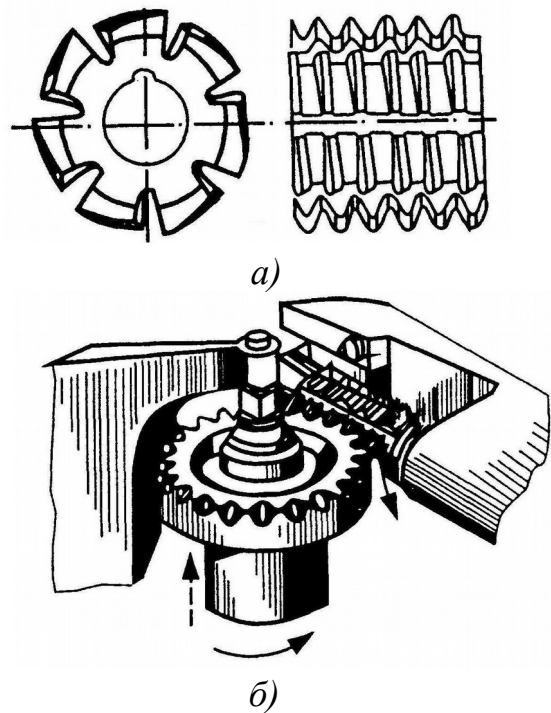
Нарізання зубчатих коліс черв'ячною фрезою
